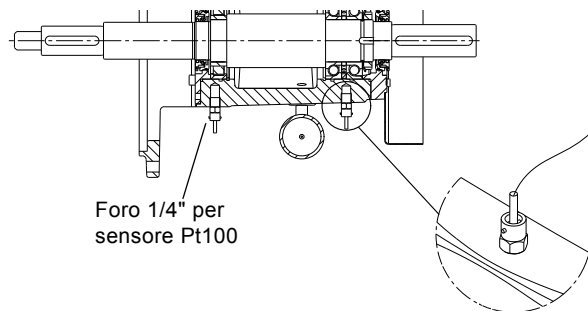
Sensori Pt100 montati sul supporto cuscinetto
